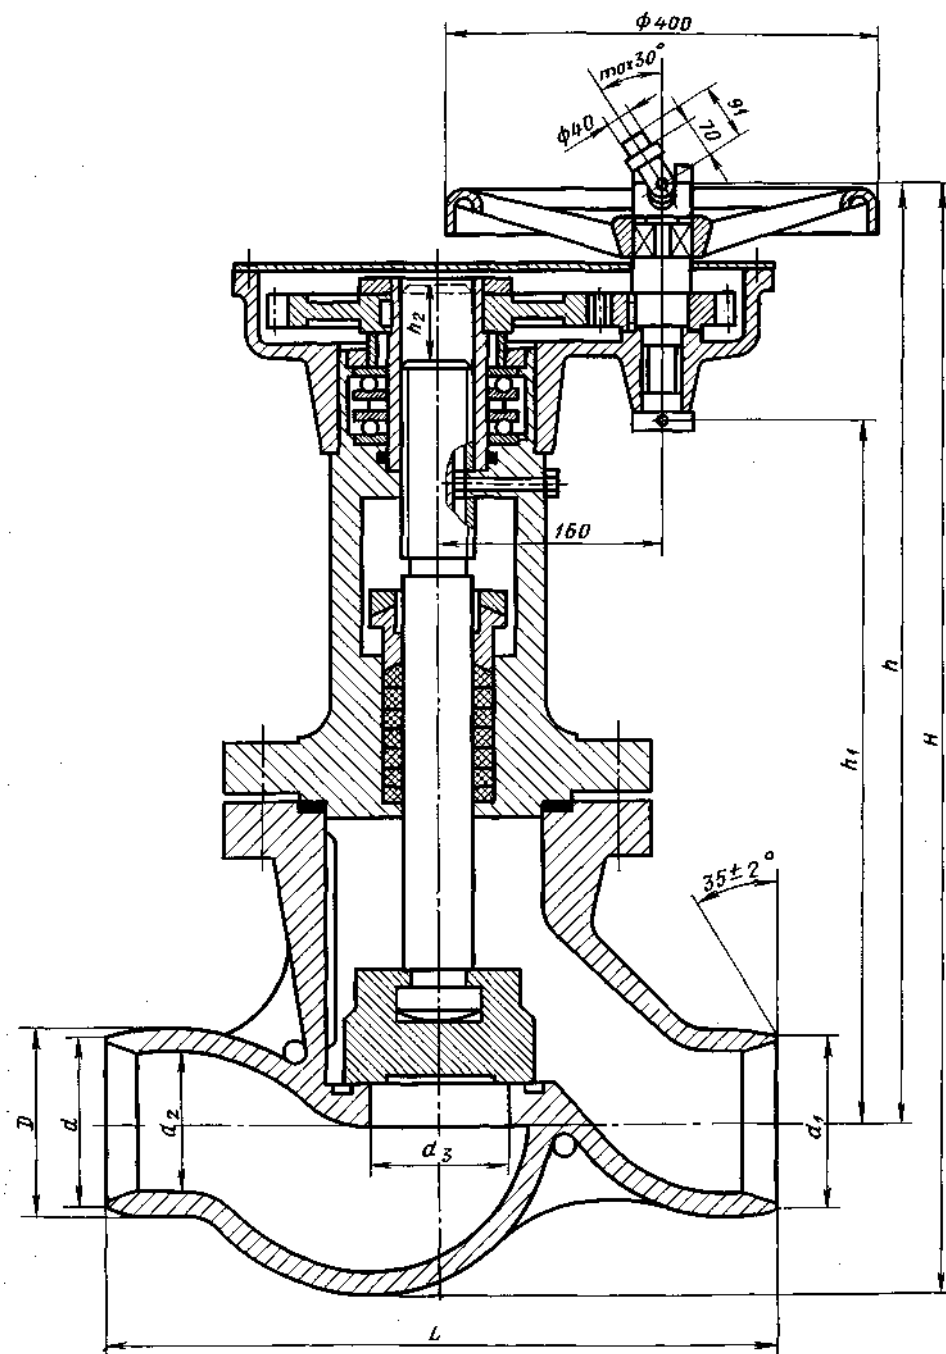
Вентиль 1с-8 с приводной головкой и цилиндрической зубчатой передачей  $D_v 80$
